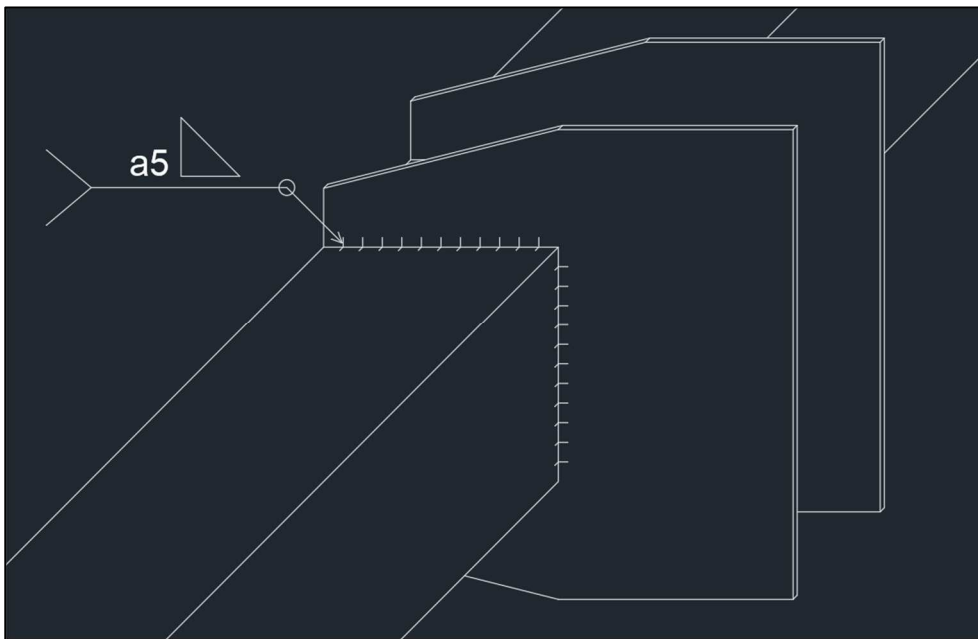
Croquis soldadura pletinas para elementos verticales.
